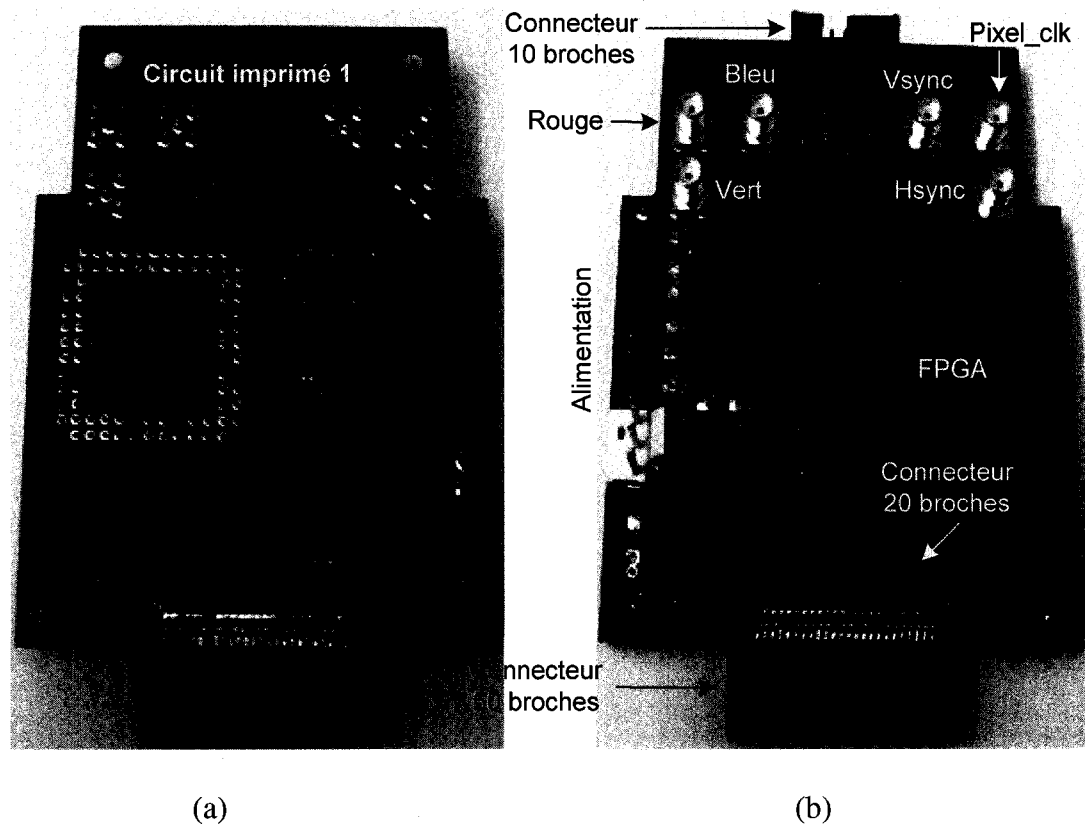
Circuit imprimé 1, a) Vue recto. b) Vue verso.
